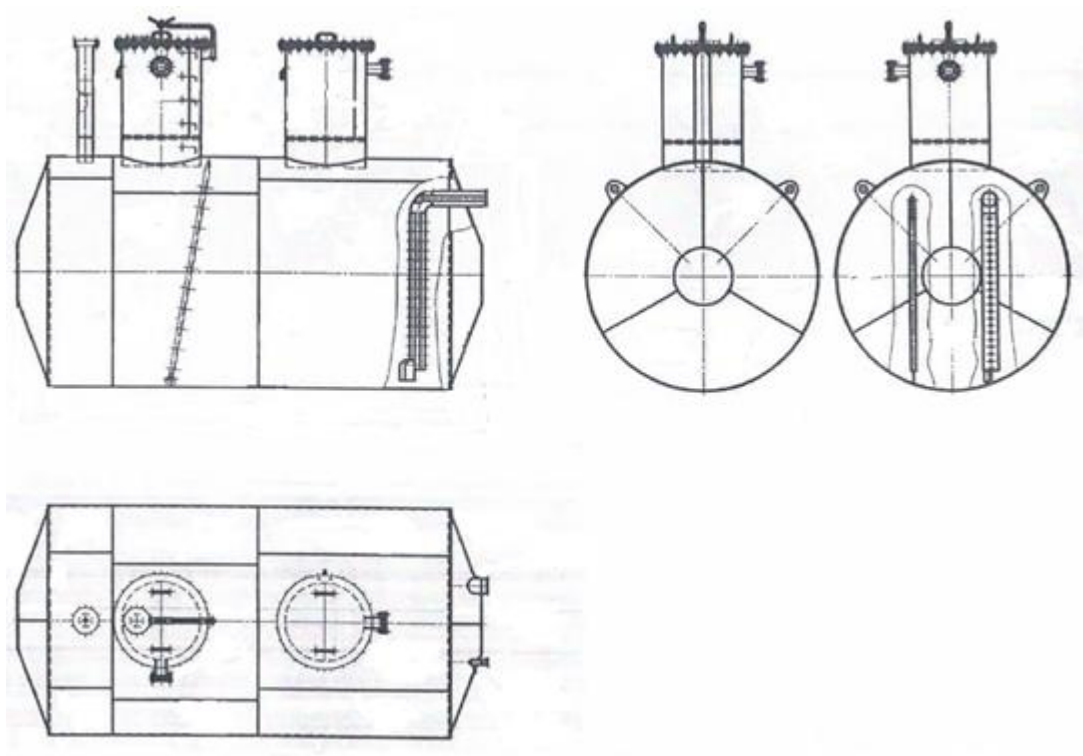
Эскиз общего вида резервуара РГС-20
